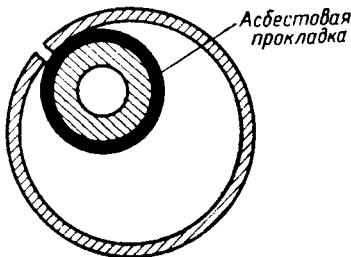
Схема сварки цилиндрических обечайек
